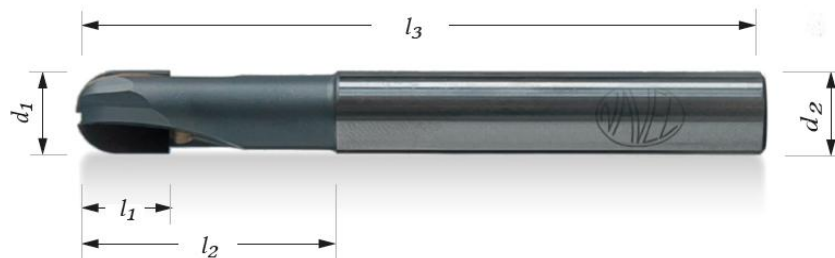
TK 4břítá fréza "AEROMILL" vysoce produktivní
